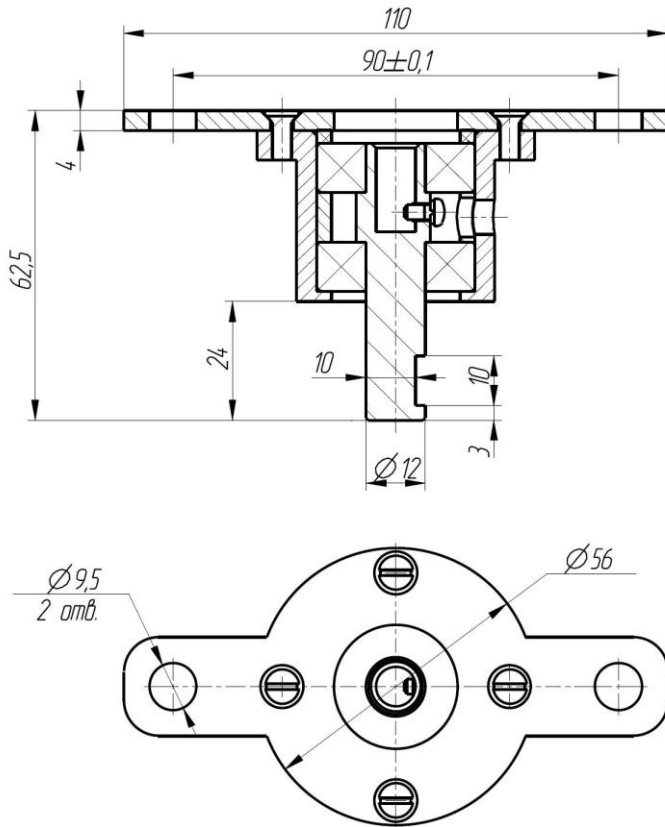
Габаритные и присоединительные размеры модуля усиления
